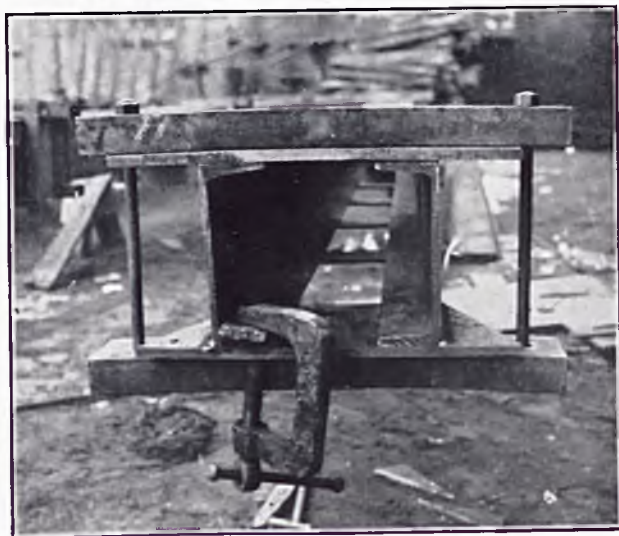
Base de la colonne préparée pour la soudure.
